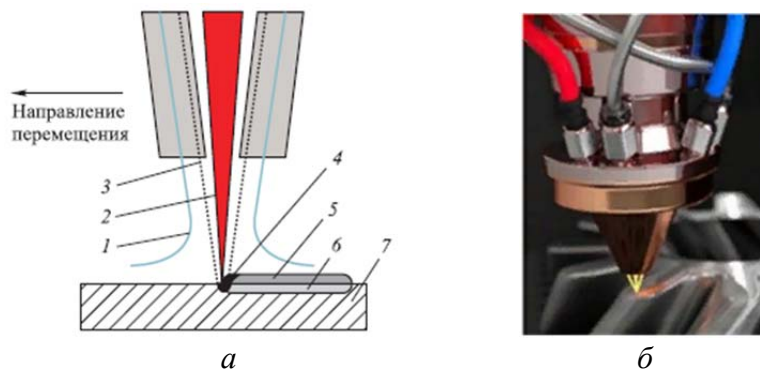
Схема (а) и фото (б) формирования объёма селективным лазерным плавлением. 1 – защитный или транспортный газ; 2 – сфокусированный луч лазера; 3 – порошок; 4 – зона расплава; 5 синтезированный слой; 6 –высокотемпературная зона; 7 – подложка или исходная заготовка, на которую наносится материал при ремонте или для получения слоя с особыми свойствами
